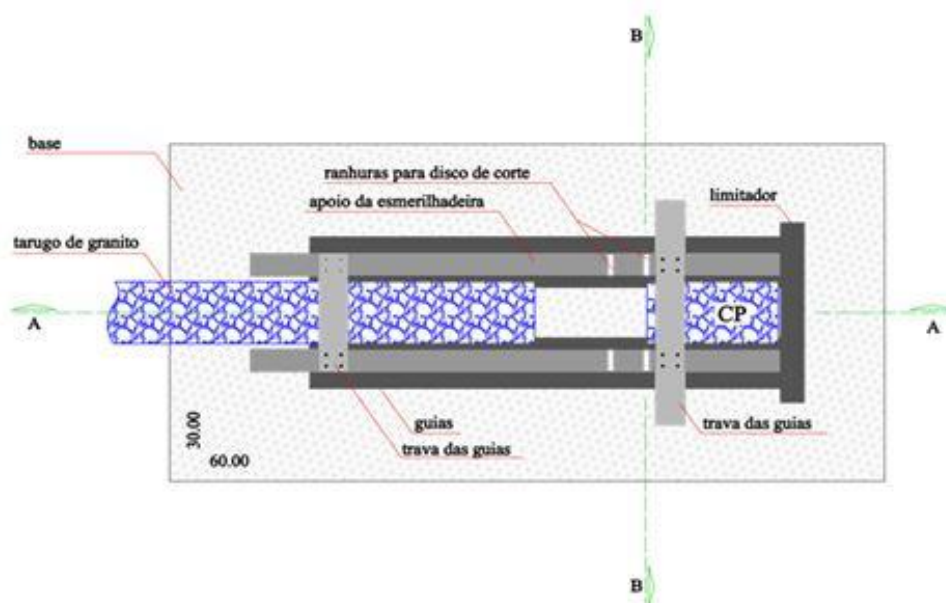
Planta do dispositivo de corte de tarugo de rocha.
